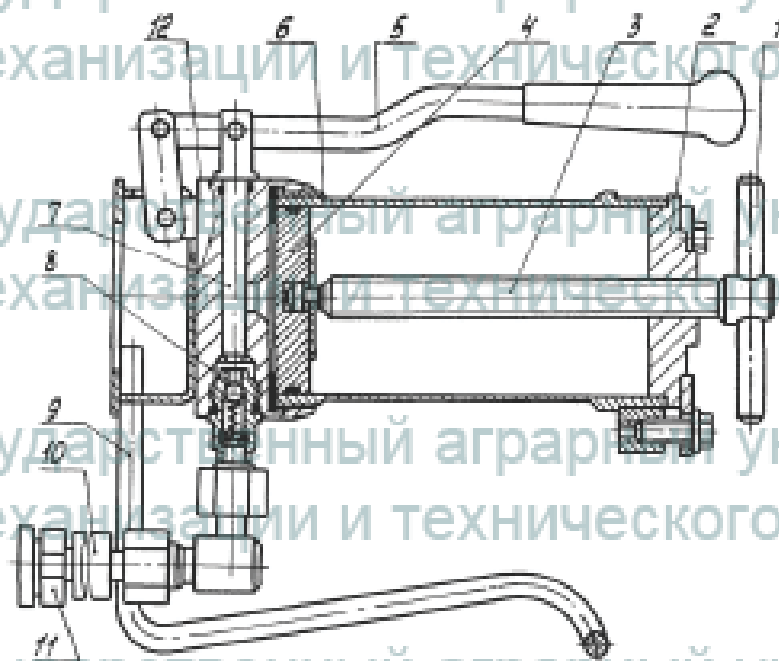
Устройство для подачи смазки (патент РФ №2244202)
